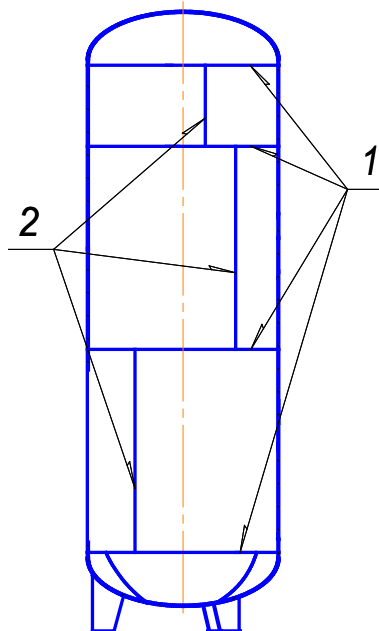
Расположение сварных швов на изделии.
